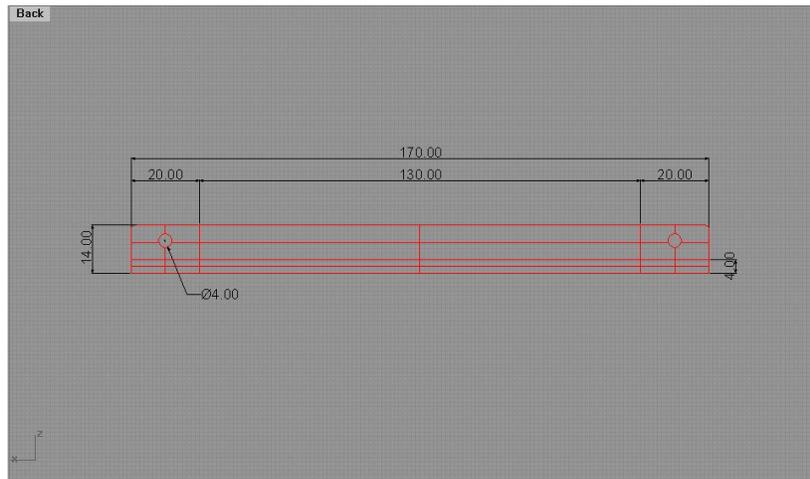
Vista lateral de las bases de anclaje 1:1 en mm.
